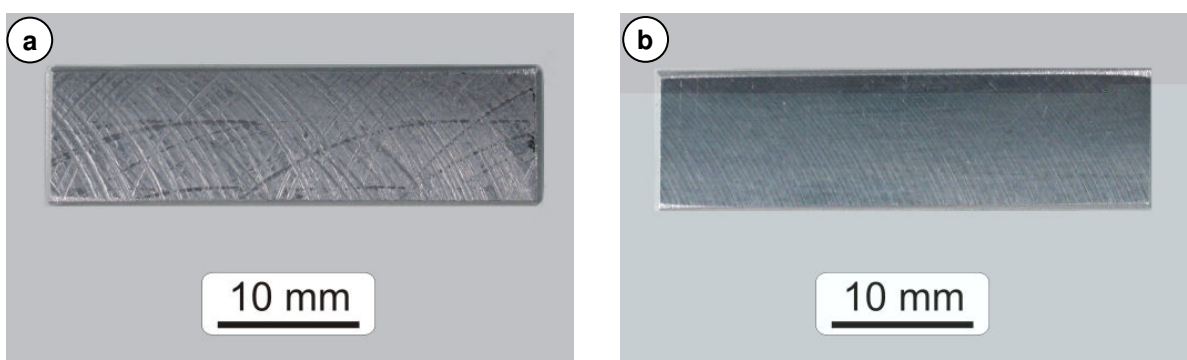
Aufsicht auf die gefräste Oberfläche konventionell bearbeiteter Werkstücke
